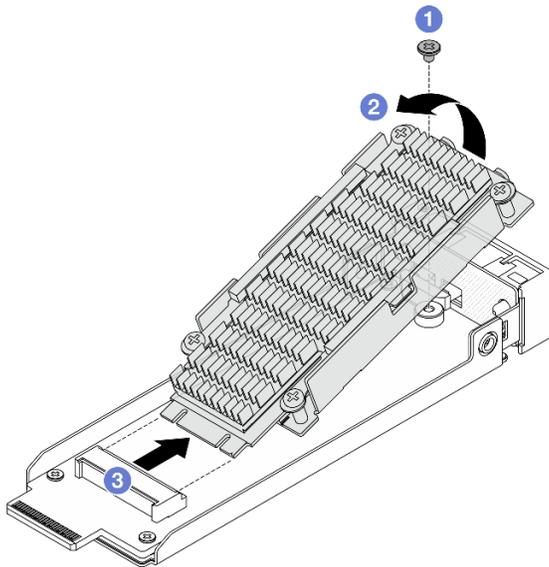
M.2-Laufwerk mit Kühlkörper entfernen
